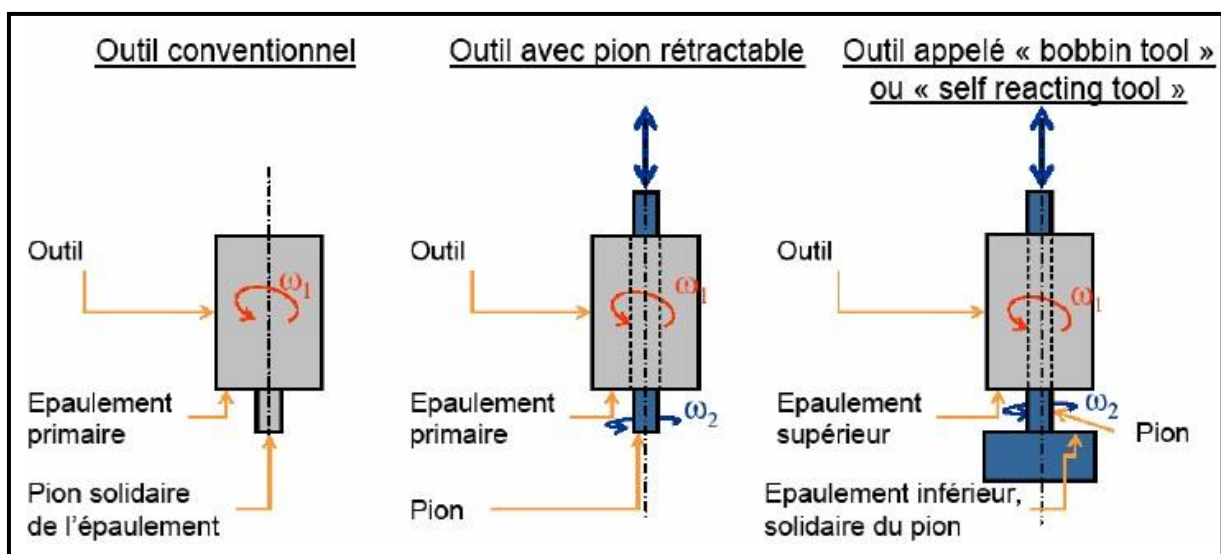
Les différentes technologies de soudage [II-10] .
